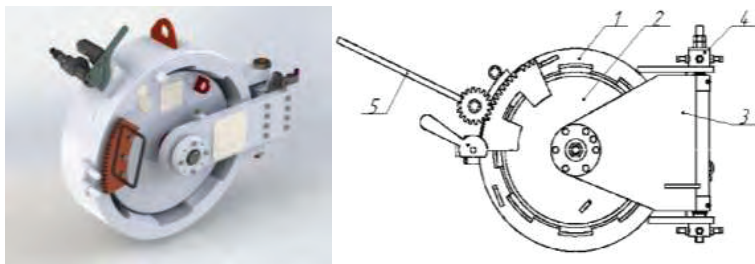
Конструкция байонетного затвора: 1 - фланец корпуса; 2 - крышка; 3 - петля; 4 - устройство поворотное; 5 - ключ с шестерней.
